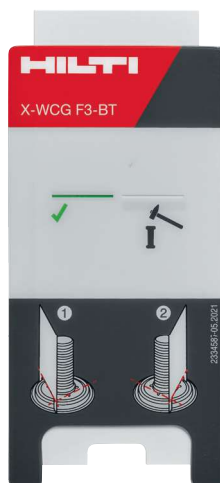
Ausrüstung für Bolzenschweißgerät – Teil II
